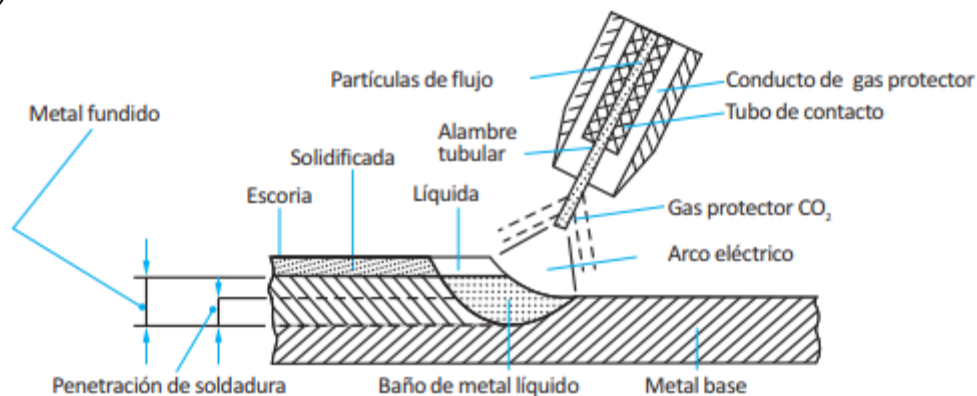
Soldadura por arco eléctrico con alambre tubular
